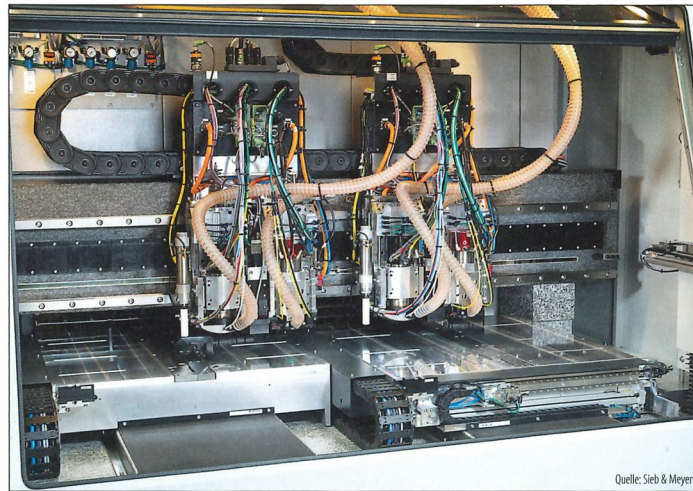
(links): Bei den Bohr- und Fräsmaschinen von Ernst Lenz Maschinenbau ist die Maschinensteuerung CNC 84.00 im Einsatz. Bild 3 (rechts): Mit dem Steuerungspaket von Sieb & Meyer kann Lenz jeden Kunden bedienen.
